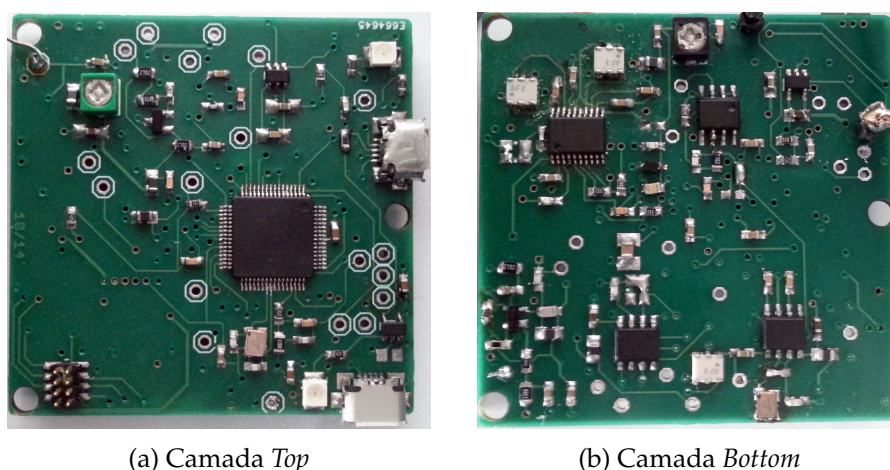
Imagem da PCB depois de construída e com os componentes soldados
